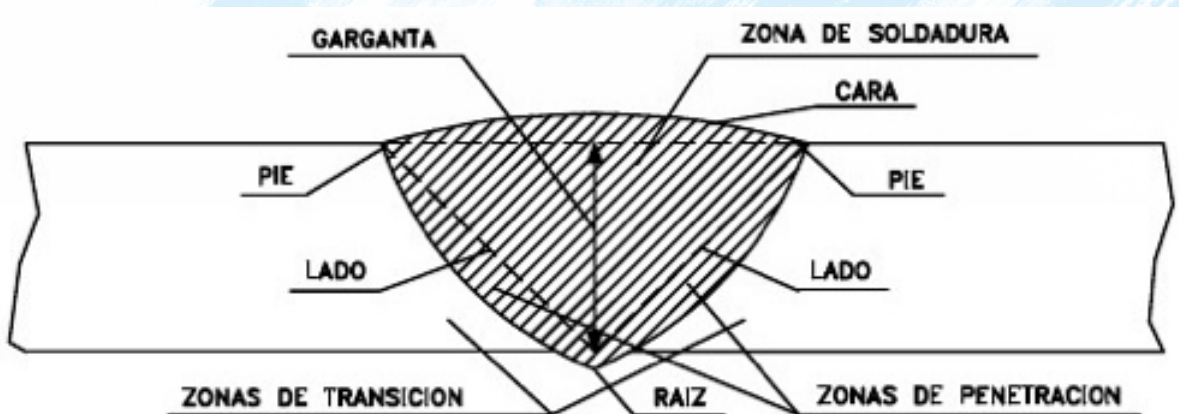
Estructura de los bordes de soldadura en el proceso de soldadura con flama oxiacetilénica
